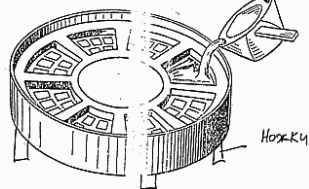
Заливка сегментов упорных подшипников баббитом
